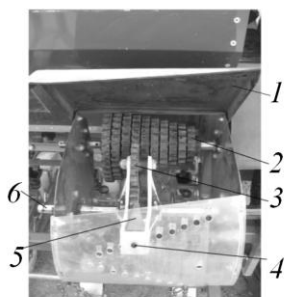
Многоступенчатая зубчатая передача (редуктор): 1 – крышка; 2 – блок зубчатых колес; 3 – подвижная каретка; 4 – стопорная кнопка; 5 – зажим рычага; 6 – вал каретки
